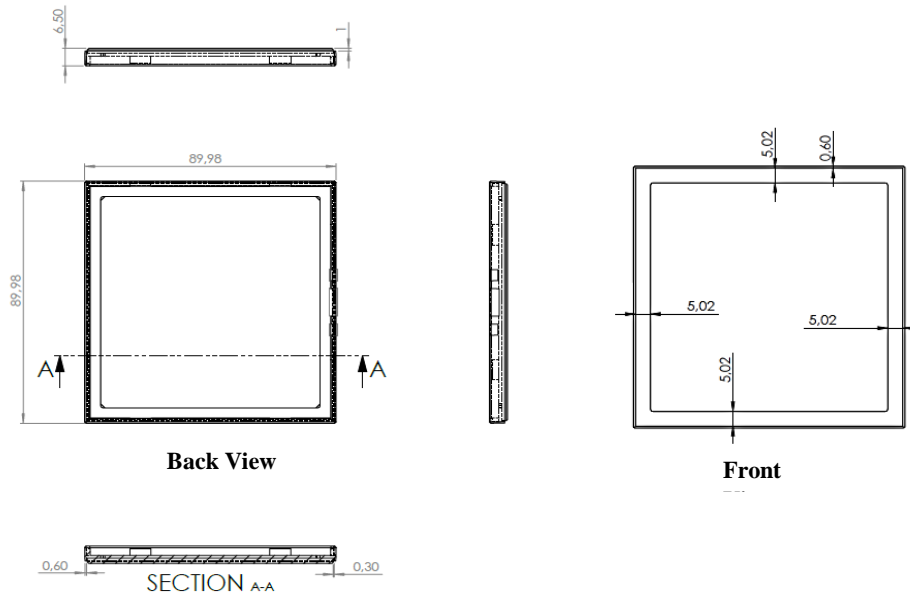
Desenho técnico da peça a desenvolver durante o projeto
